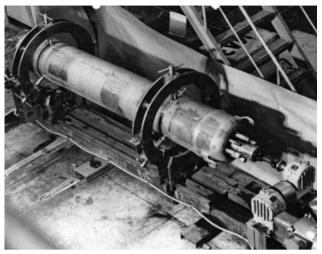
Общий вид станка для вскрытия и резки корпуса ИИН-1
